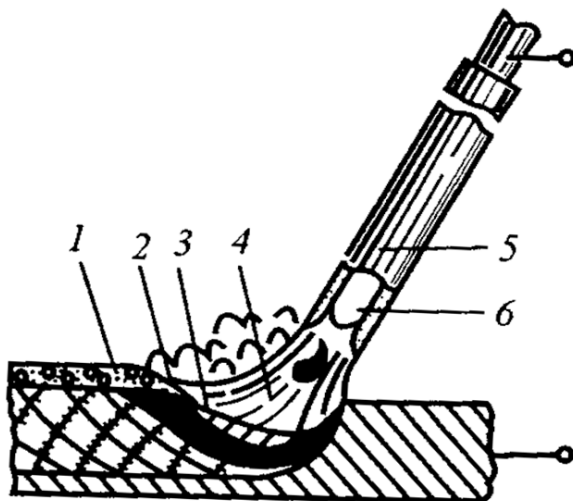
Схема ручного дугового зварювання покритим електродом:
